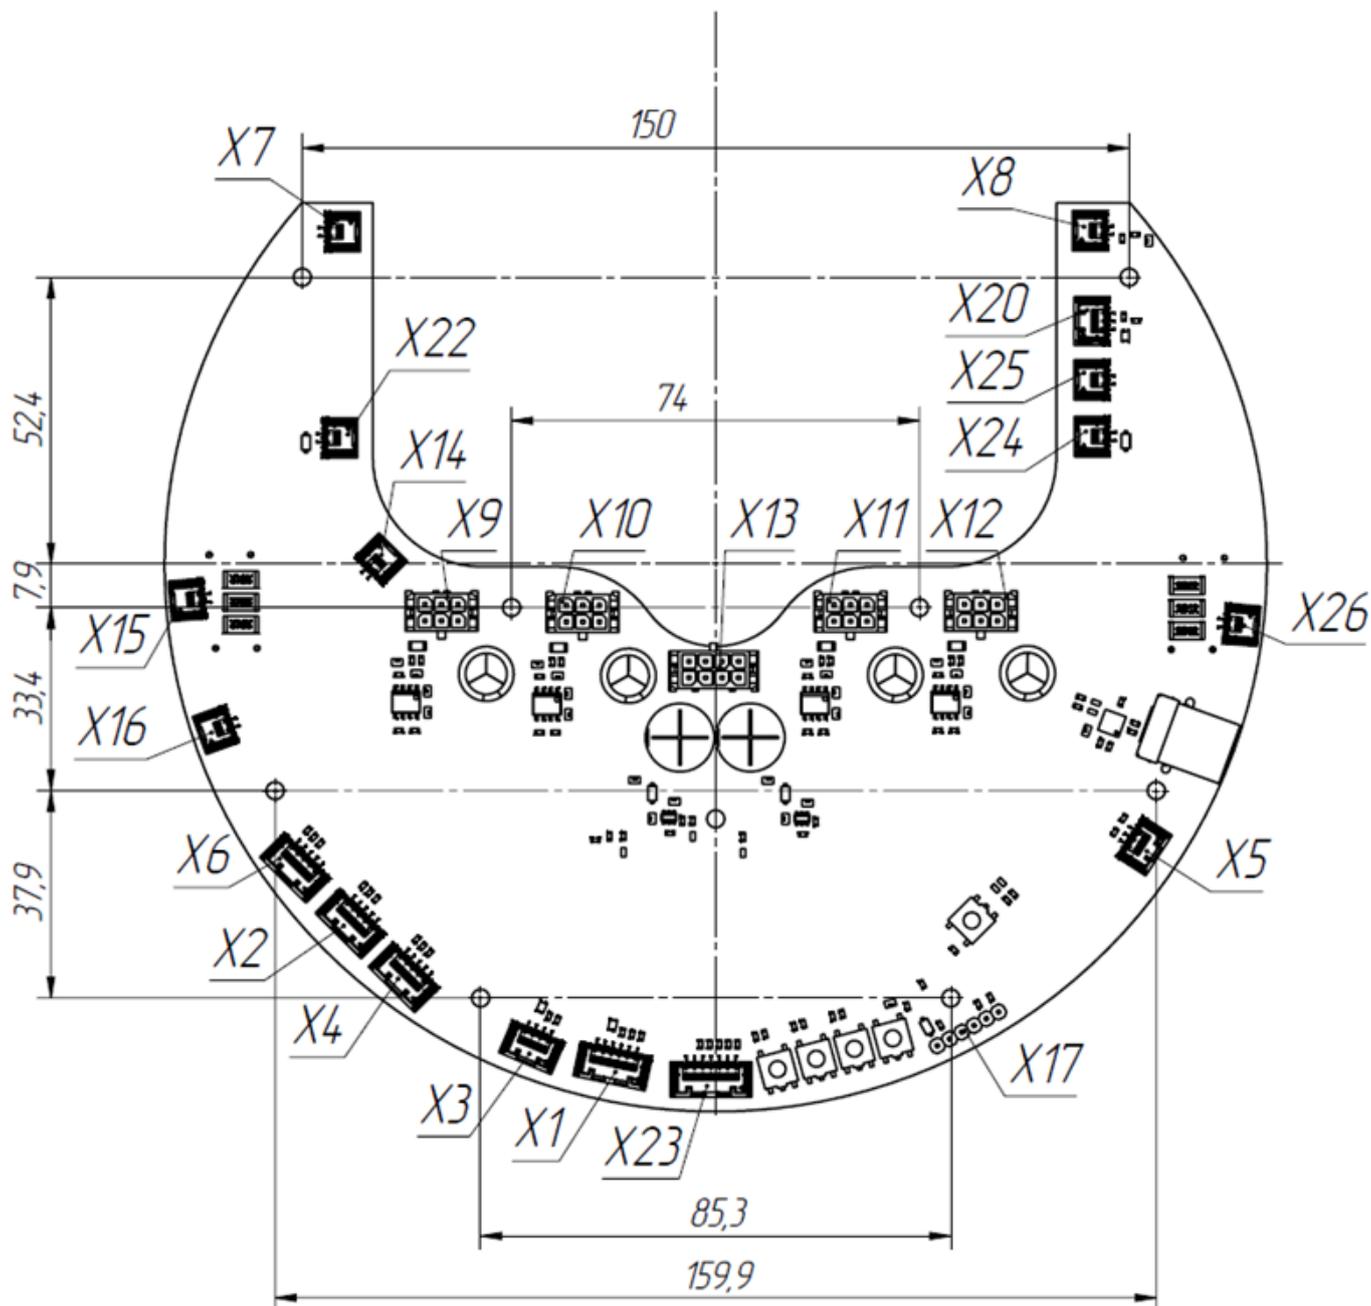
Габаритный чертёж материнской платы. Компоновка элементов.
